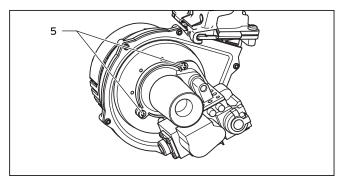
Vissage mécanisme gaz/ventilateur
